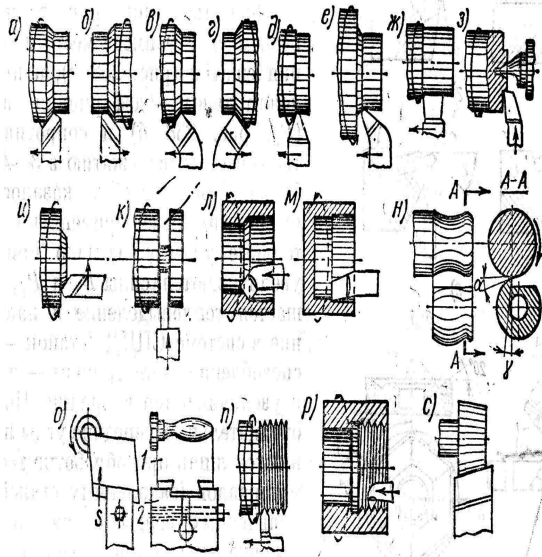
Види обробки поверхнь на токарному верстаті:
